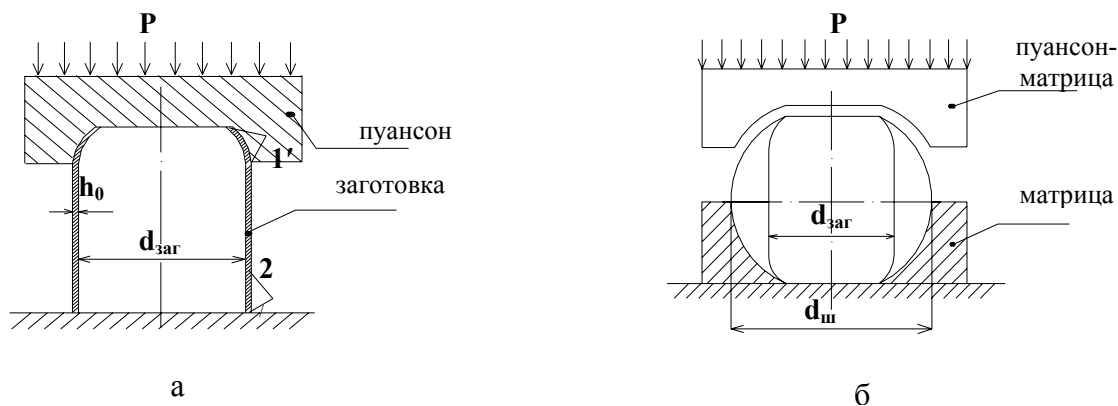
Расчетные схемы продольного обжатия сварной трубчатой заготовки (а), осадки (б)
